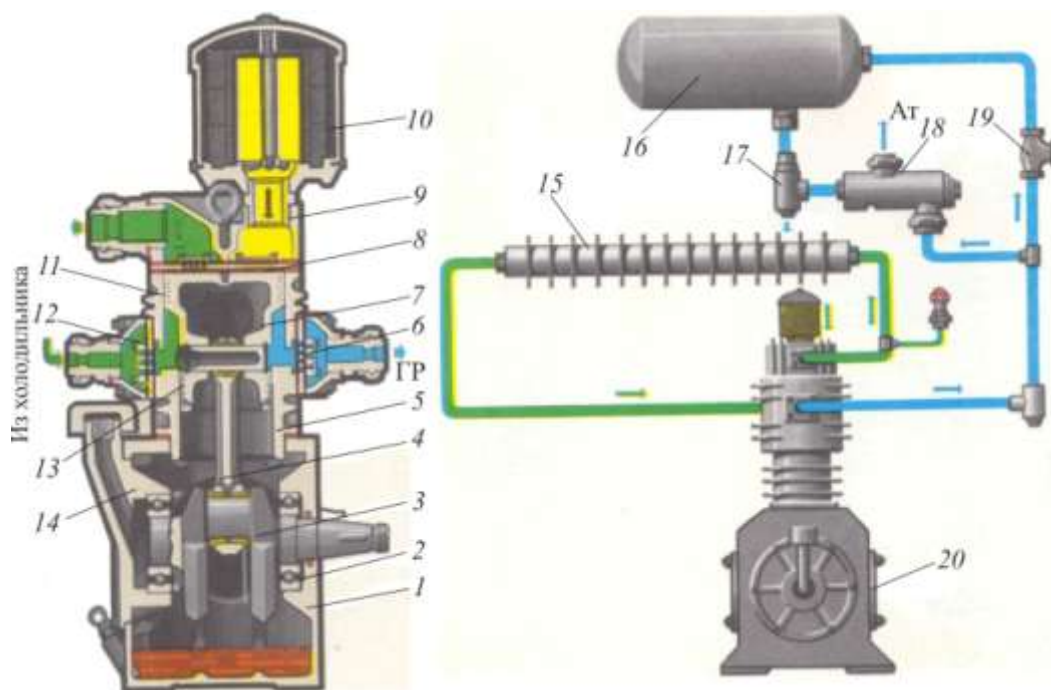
Устройство двухступенчатого компрессора типа ВВ-1,5/9:
